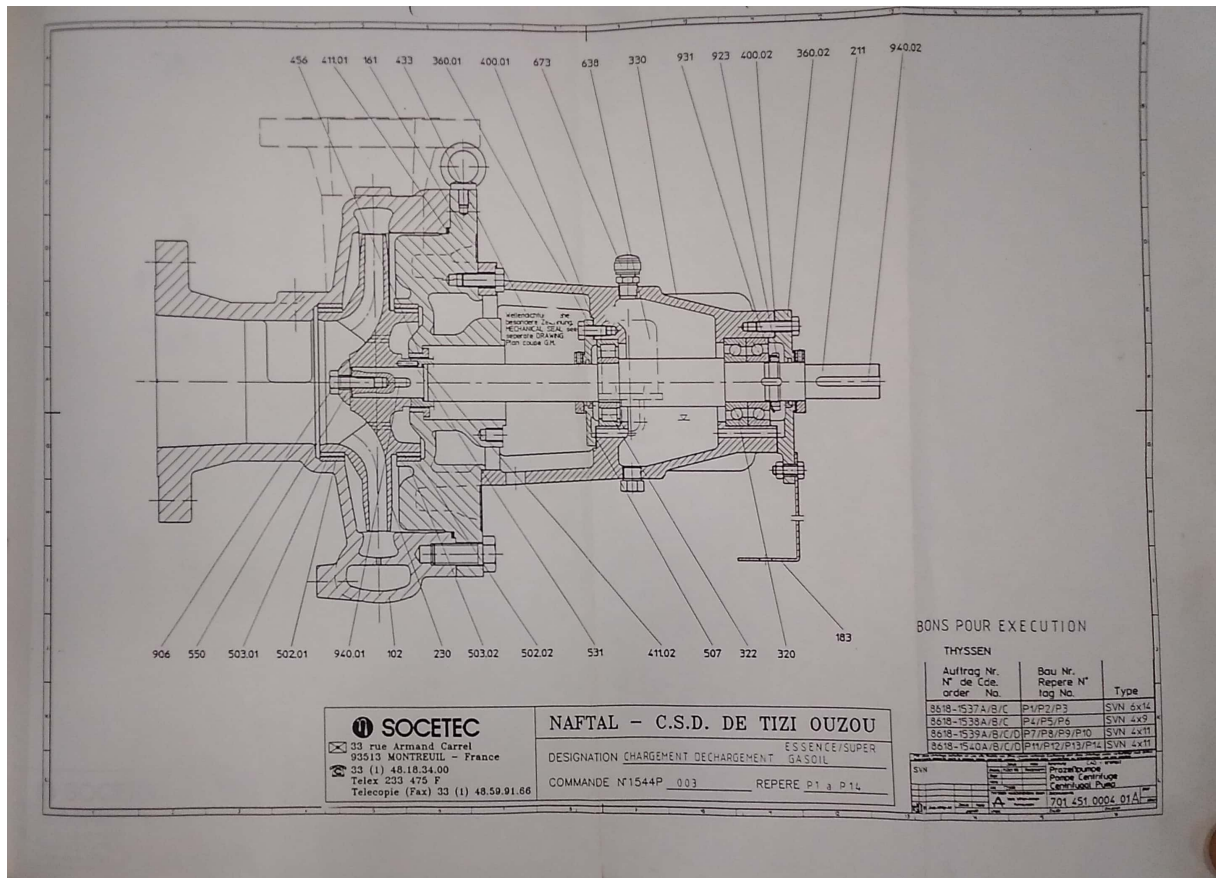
Dessin de coupe et liste des pièces de la pompe centrifuge P4.
